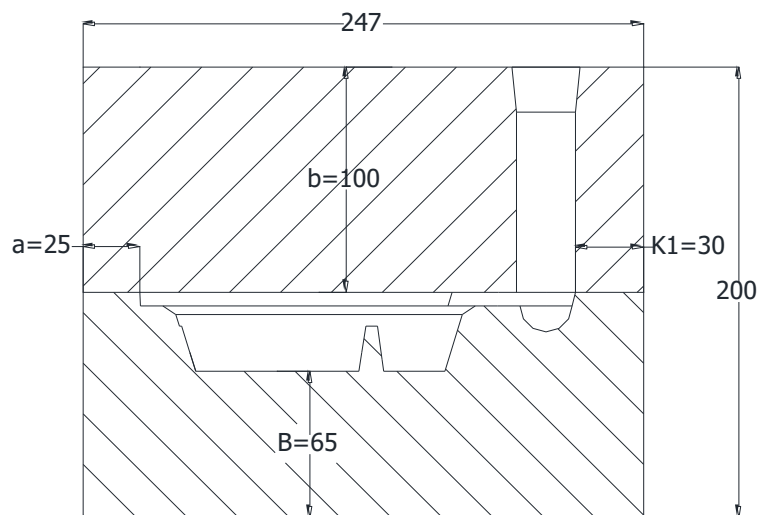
25. Vista frontal del modelo del quemador B (tapa) acoplado con la caja de moldeo.
